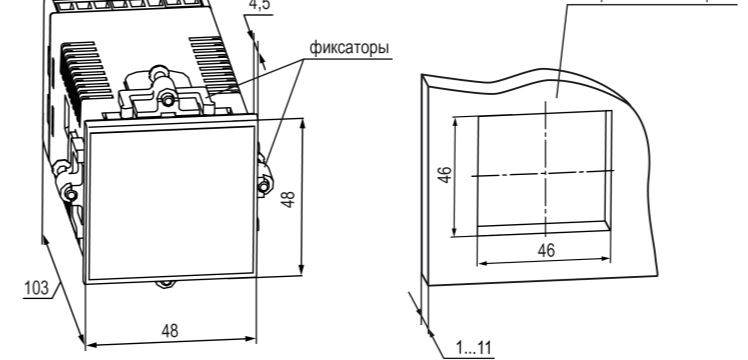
Габаритные размеры корпуса Щ5 и монтажного отверстия в щите
